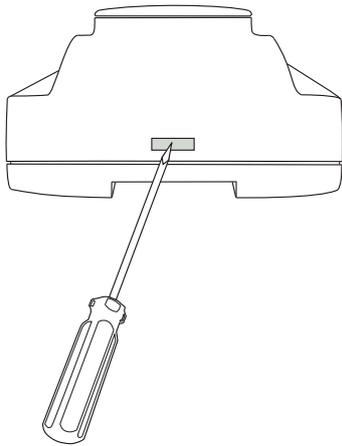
Entfernen Sie die Oberseite des Gehäuses (Beispiel zeigt EXOcompact Ardo/Eedo).
